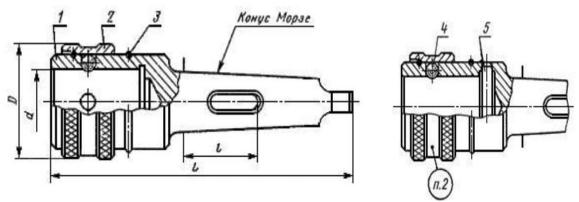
Патрон быстросменный (ГОСТ14077 — 83): 1 — корпус; 2 — кольцо; 3 — пружинное кольцо; 4 — шарик; 5 — цилиндрический штифт
